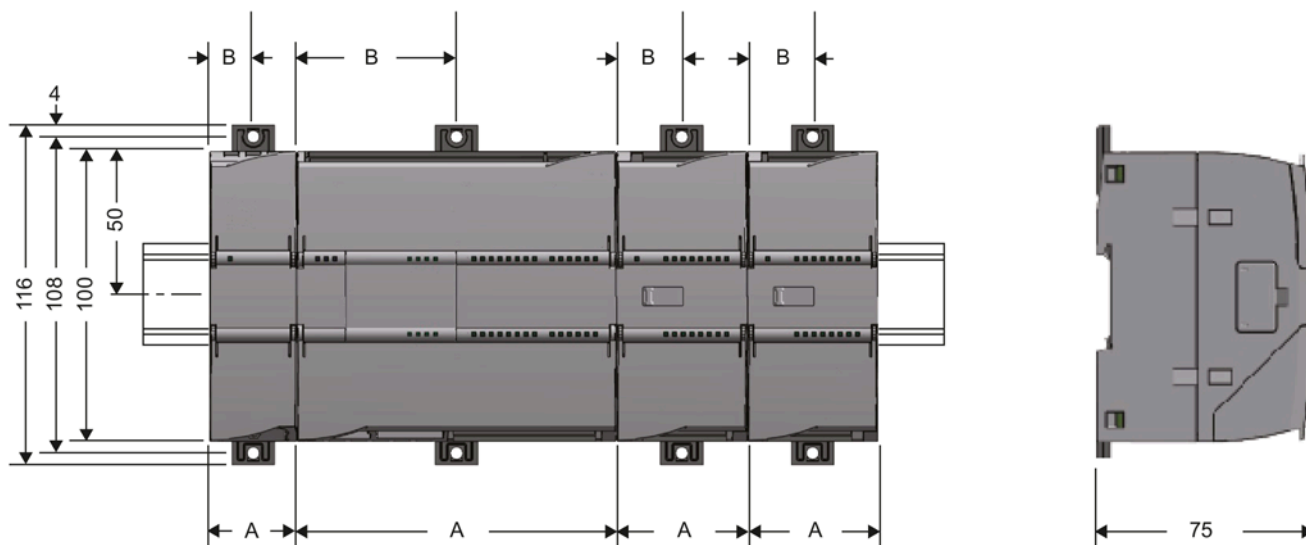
Dimensioni di montaggio dell'S7-1200
